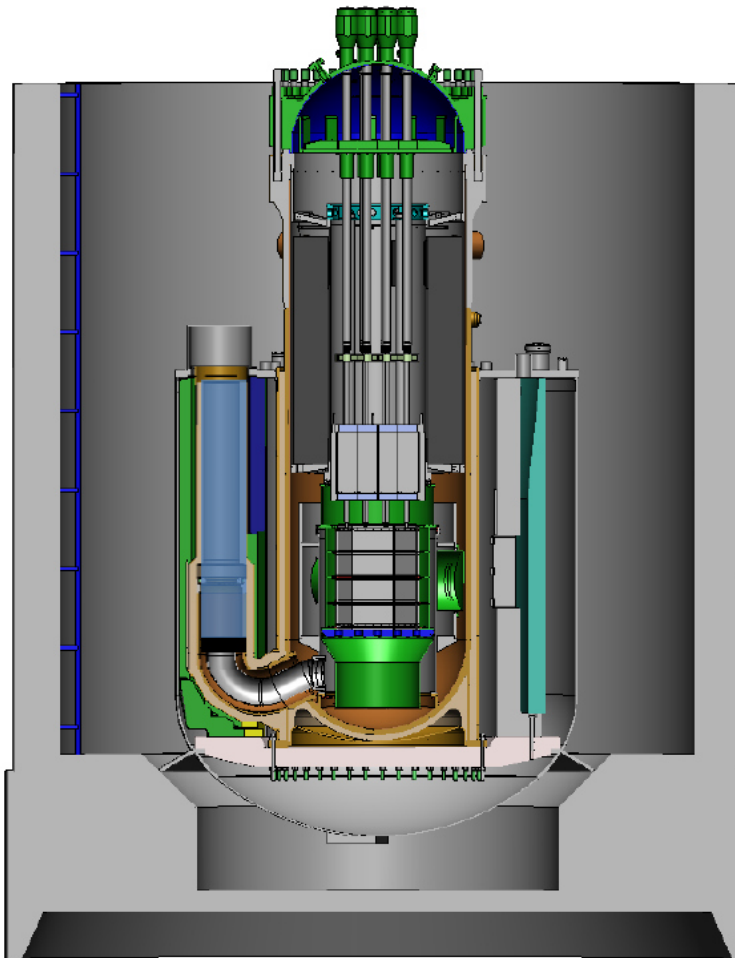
Zustand nach Ausbau der Hauptkühlmittelpumpe, Setzen des Dichtstopfens und Fluten des Pumpenrohrs
